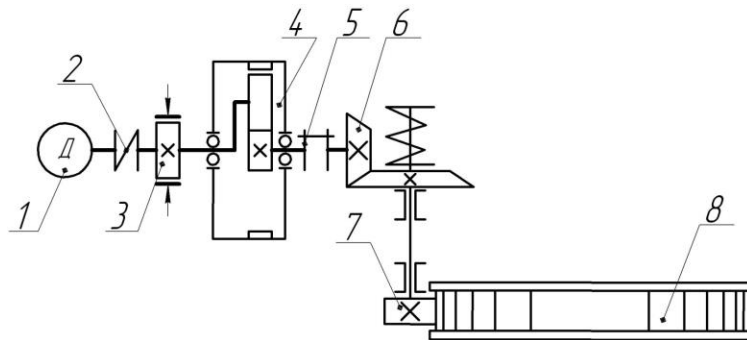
Кінематична схема механізму повороту: 1 – електродвигун; 2 – пружна муфта; 3 – гальмо; 4 – планетарний редуктор; 5 – муфта; 6 – конічна зубчаста передача; 7 – відкрита циліндрична зубчаста передача; 8 – поворотна частина
